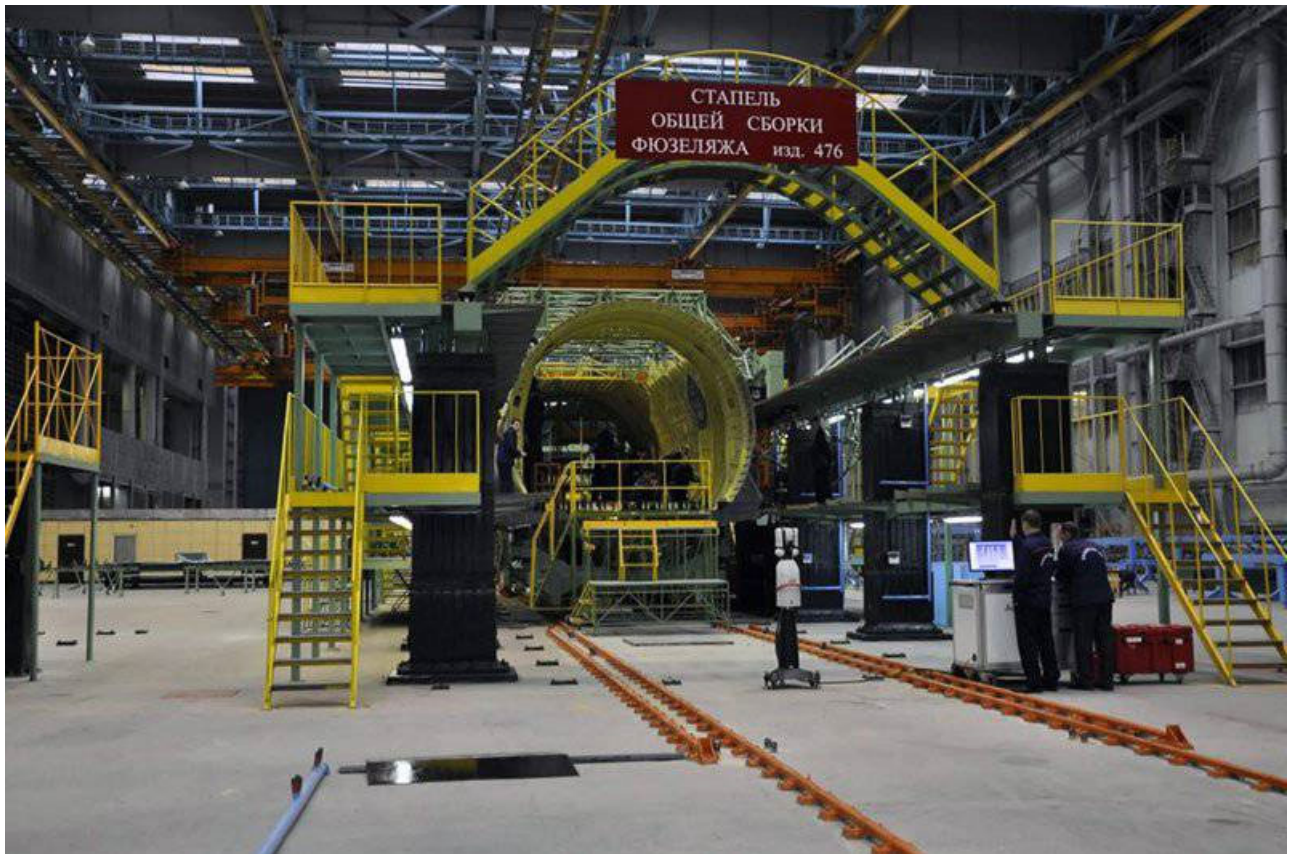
Сборочное приспособление «Стапель общей сборки»
